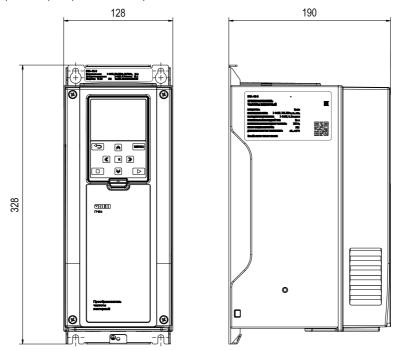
Габаритные размеры прибора в корпусе 1
